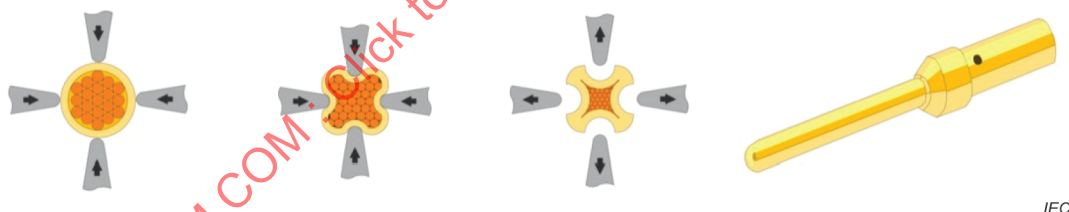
Procédé de sertissage à 4 empreintes avec des outils réglables
